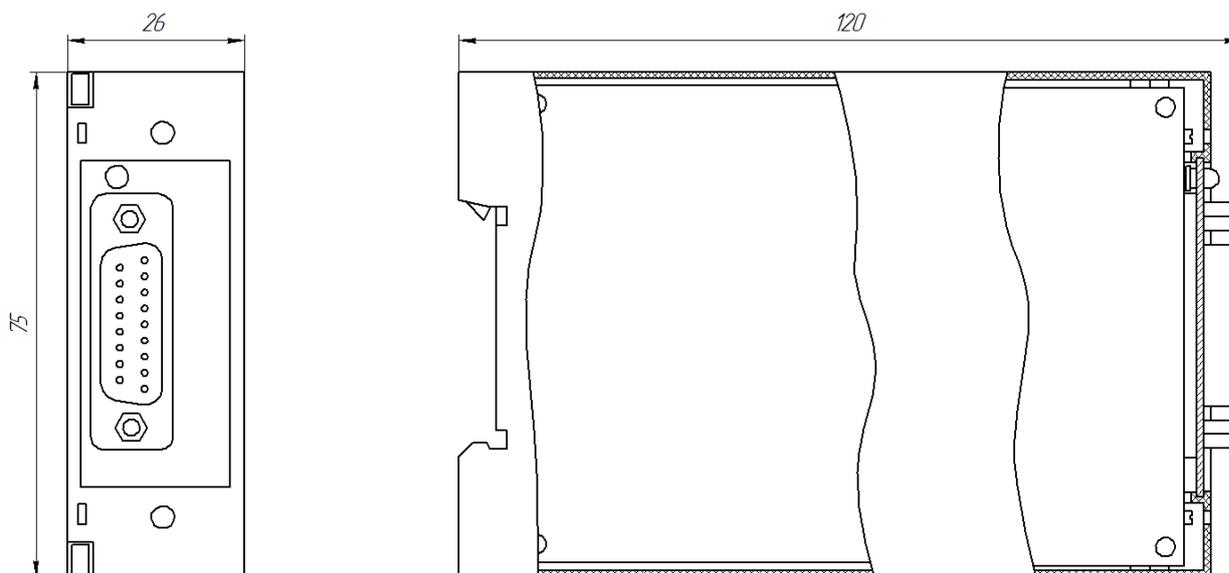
Зовнішній вигляд та габаритні розміри БПО-42
